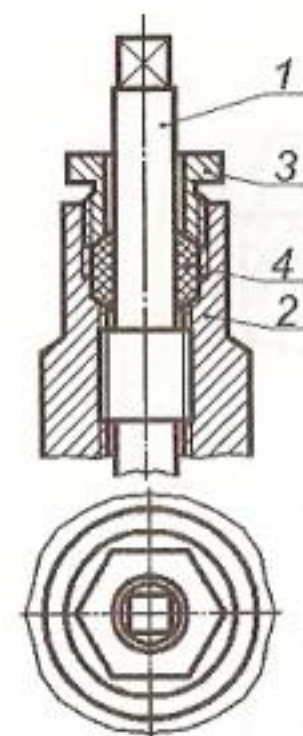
Конструктивный вариант сальникового устройства с резьбовой втулкой (фрагмент вентиля: 1 – шпindel; 2 – корпус; 3 – втулка резьбовая; 4 – уплотнитель)
